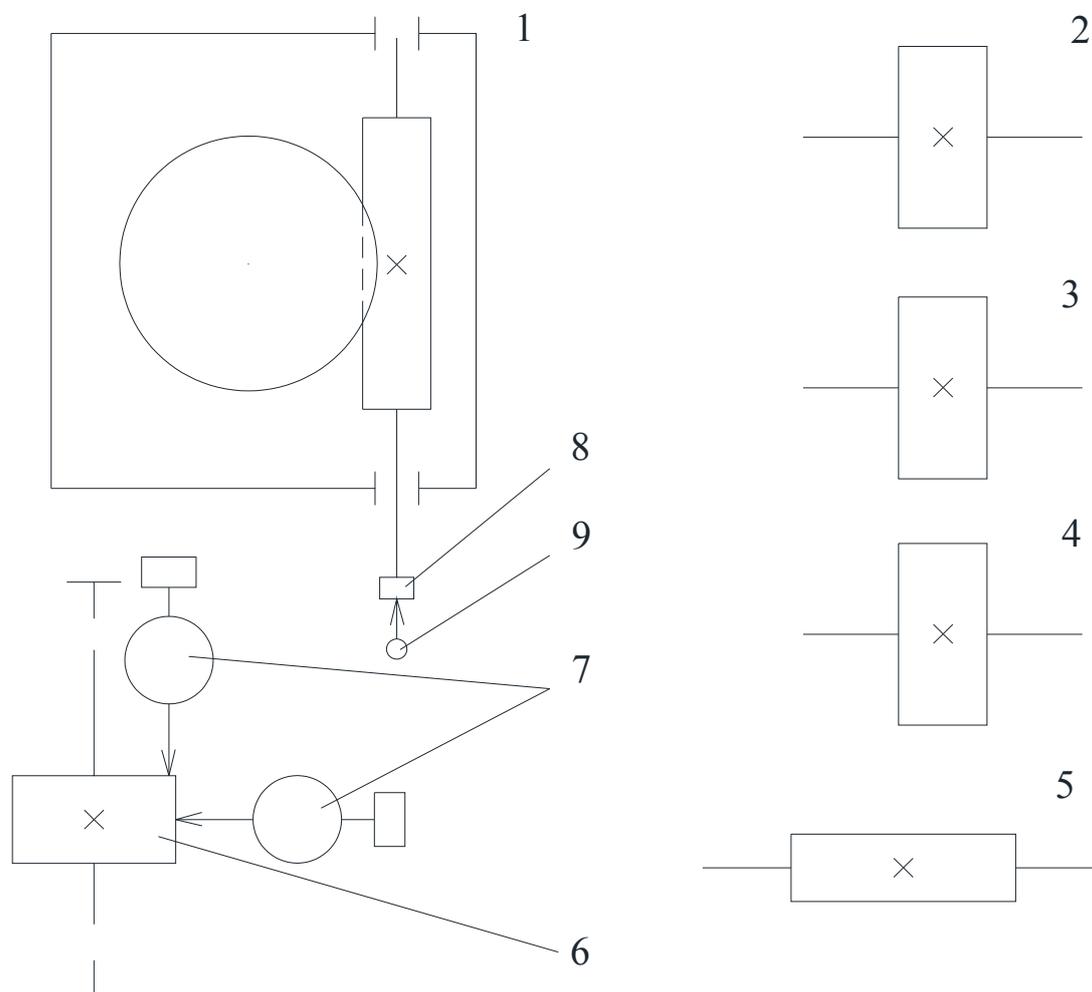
Схема станка для монтажа и выверки конических зубчатых передач: 1 – червячный редуктор; 2, 3, 4 – зубчатые колеса с видами дефектов; 5 – червяк; 6 – зубчатое колесо с торцовым радиальным биением; 7 – индикатор; 8 – градуированный лимб; 9 – стрелка
